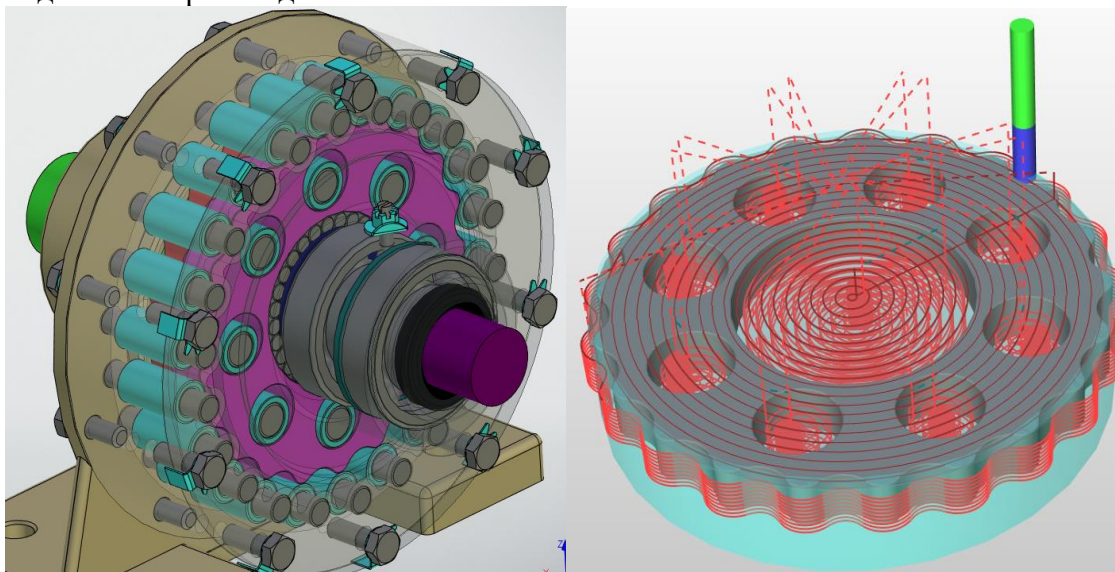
Конструкторско-технологическая подготовка производства планетарно-цевочного механизма
